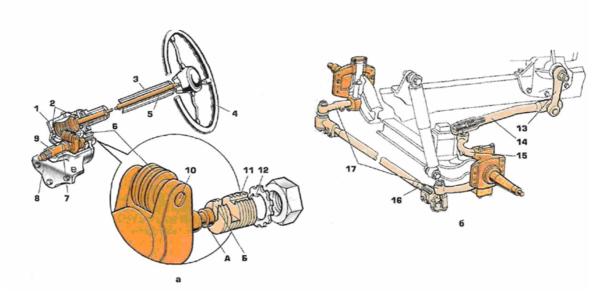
Рулевой механизм la) и рулевой привод (6) автомобиля ГАЗ:
